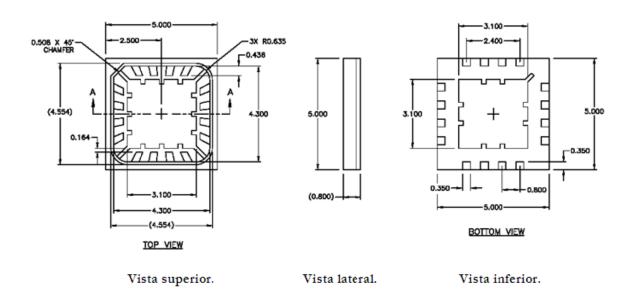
Dimensiones del encapsulado QFN16 de 5x5 mm.
